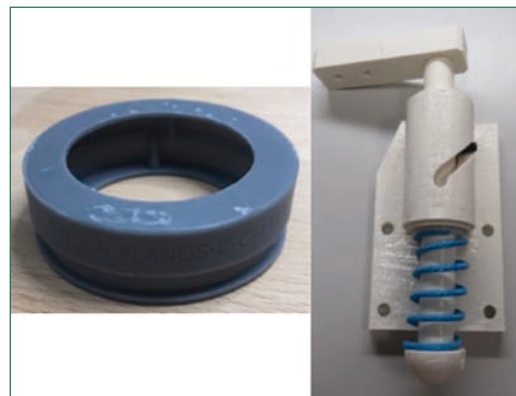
Ejemplos de pieza impresa en 3D para equipos de fabricación.
